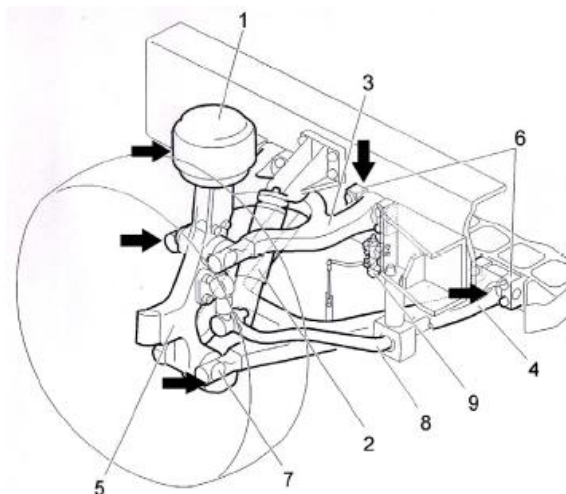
Пневмоподвеска управляемой оси автобуса и основные места её контроля: 1 – пневморессора; 2 – амортизатор; 3 – верхний рычаг; 4 – нижний рычаг; 5 – опорная стойка; 6, 7 – резинометаллические втулки; 8 – стабилизатор поперечной устойчивости; 9 – кран управления подвески.
